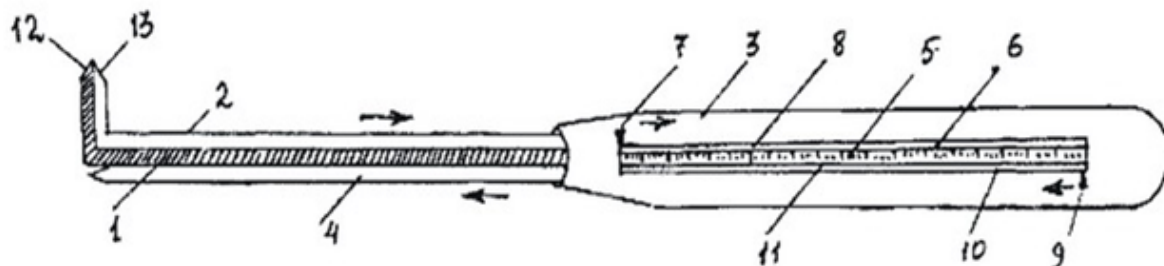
Схематическое изображение анатомического измерителя: 1 – неподвижный стержень; 2 – подвижный стержень; 3 – рукоятка; 4 – стержень глубиномера; 5 – шкалы; 6 – верхняя грань; 7 – рычаг подвижного стержня; 8 – паз для рычага подвижного стержня; 9 – рычаг глубиномера; 10 – паз для глубиномера; 11 – нижняя грань шкалы; 12 – неподвижный отметчик; 13 – подвижный отметчик
